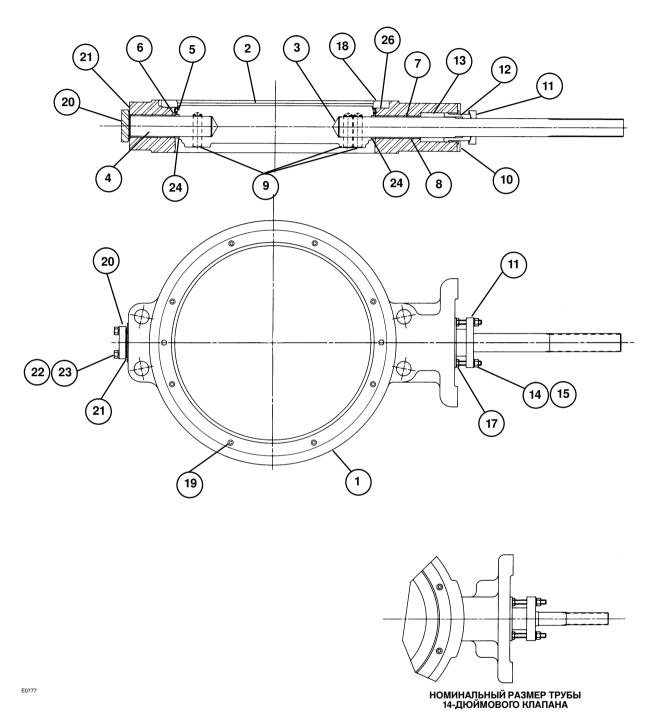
Бесфланцевый корпус клапана модели 8532
